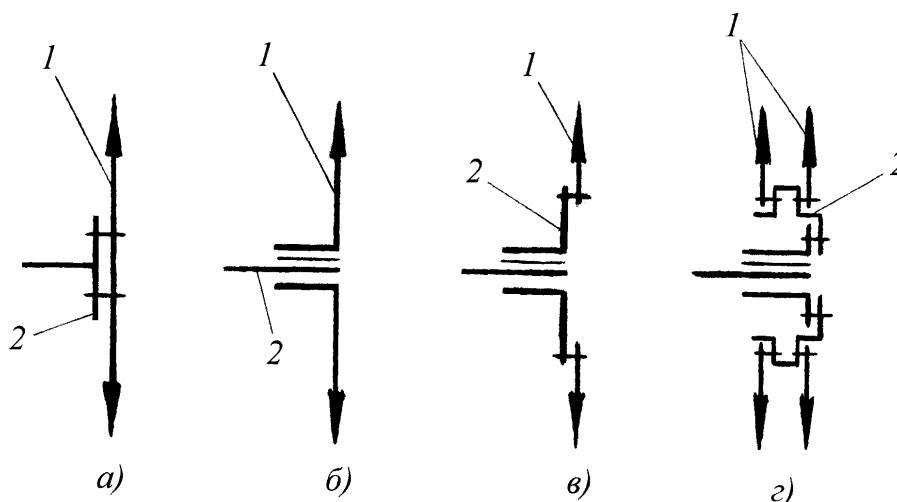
Конструктивные схемы ведущих колес гусеничного трактора
